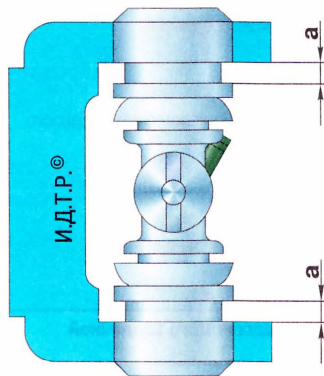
Схема запрессовки подшипников карданного шарнира
